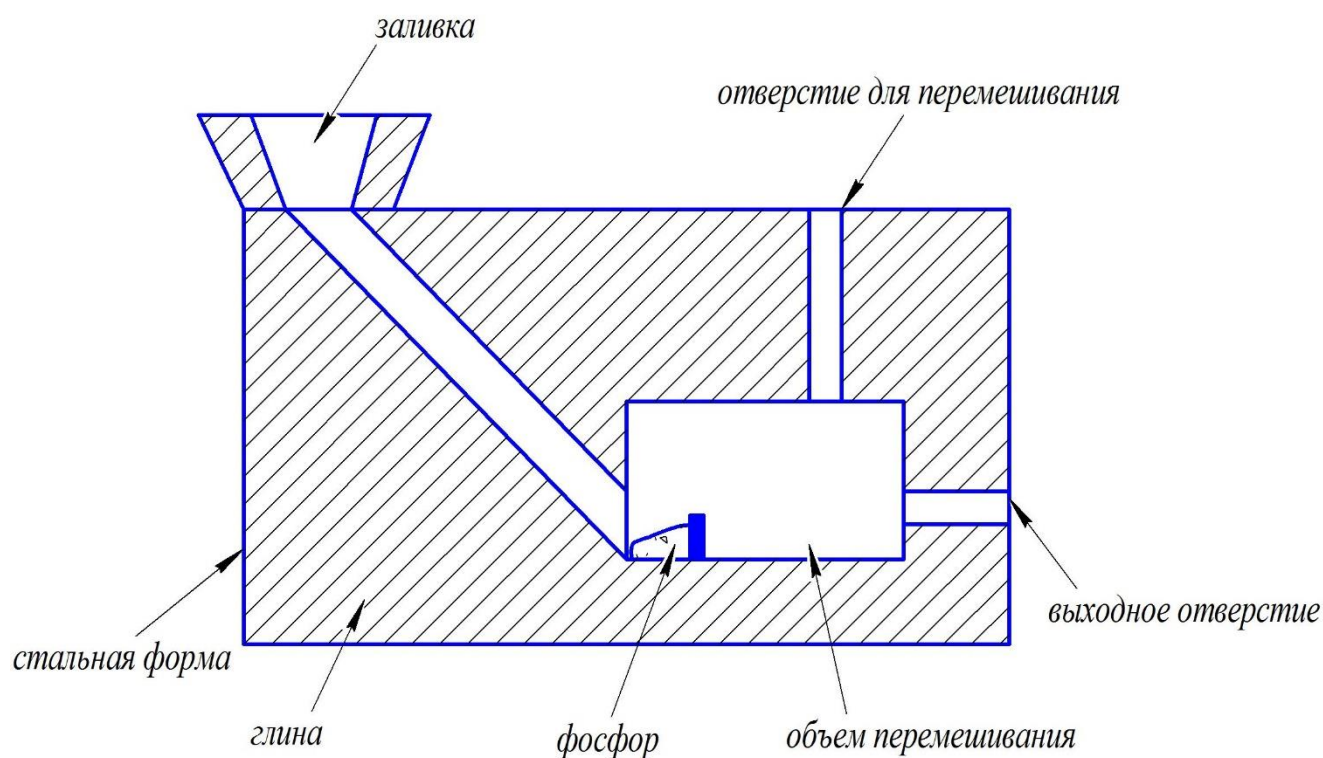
Конструкция реакционной камеры для приготовления сплава Cu-P
